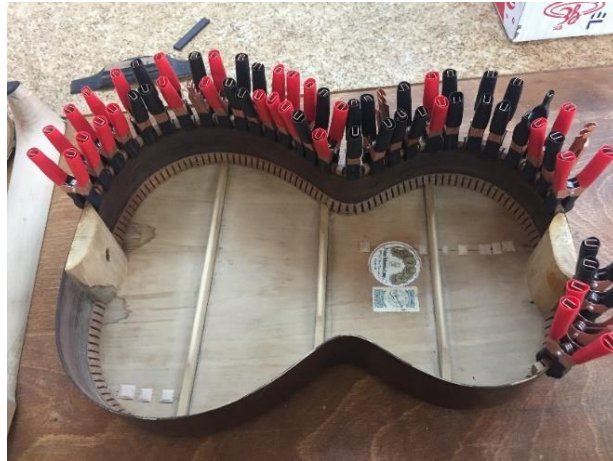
Ön tahta kirişlerinin yapıştırılması.
